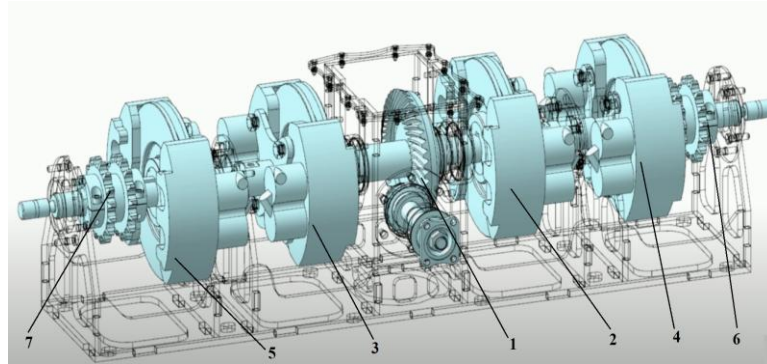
Редуктор в маточині колеса [17]
